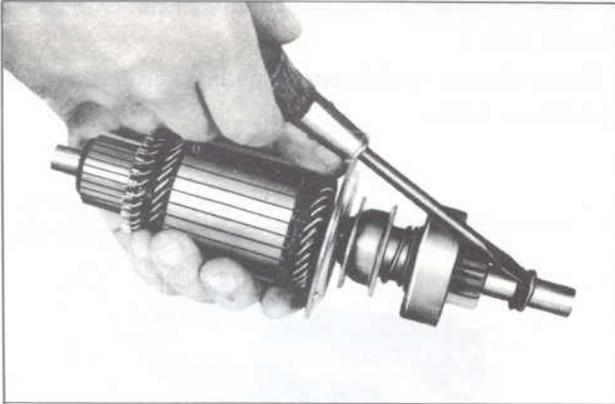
Remoción del conjunto del embrague de sobremarcha
